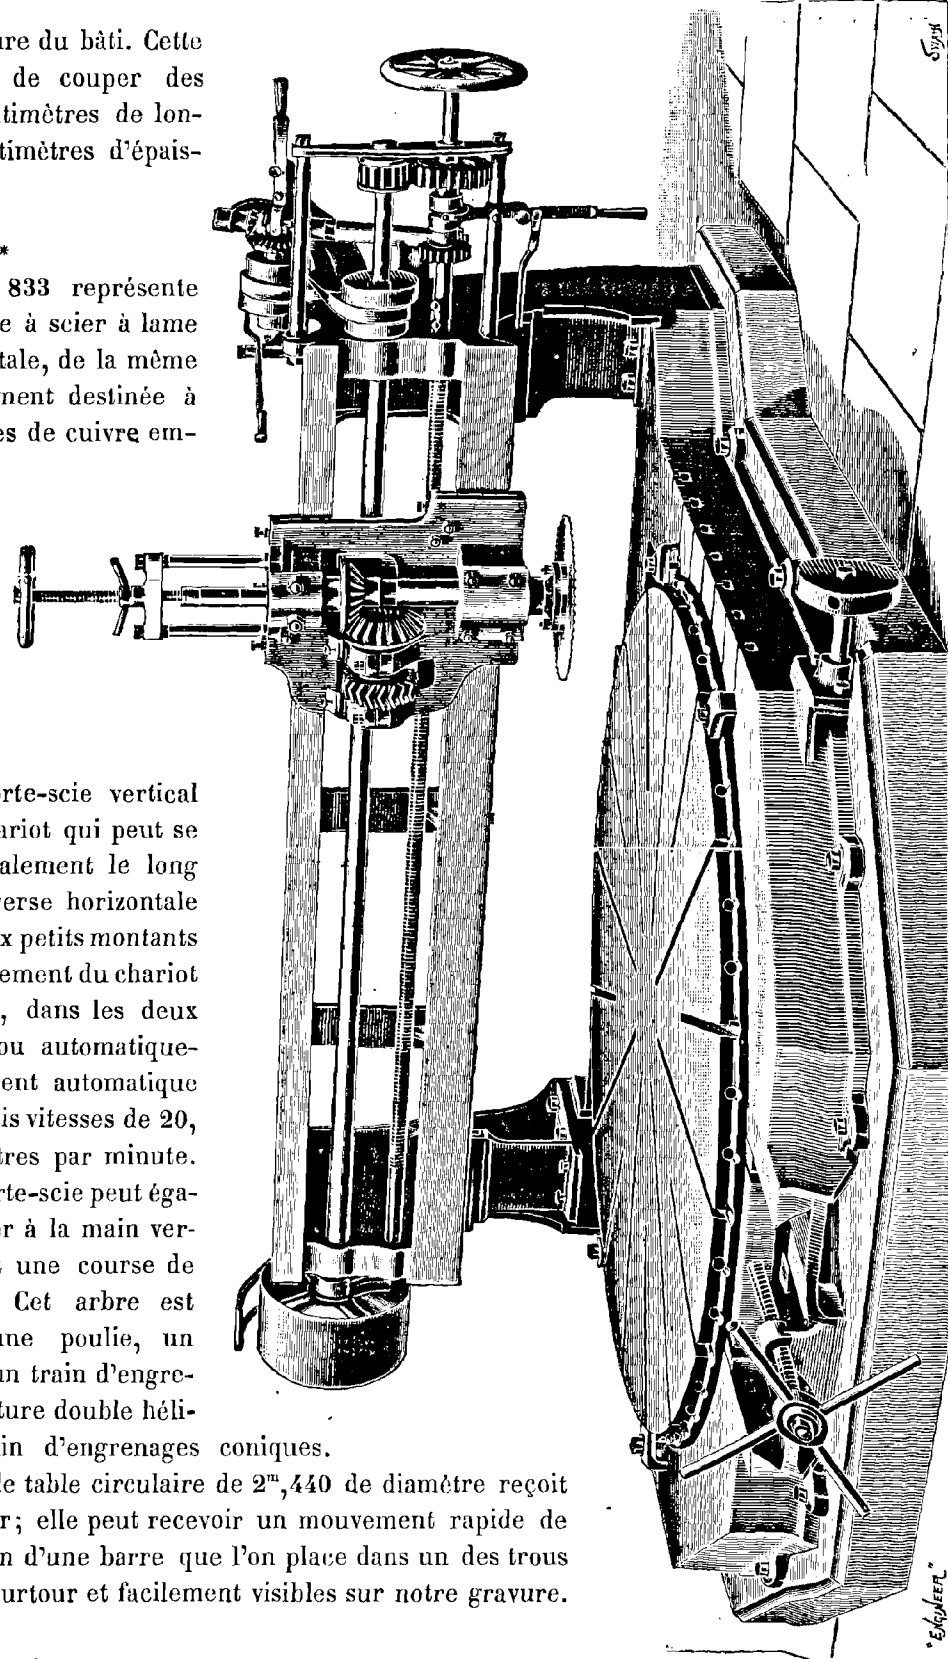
Machine spéciale à lame horizontale pour plaques de cuivre embouti de M. Lucas.
